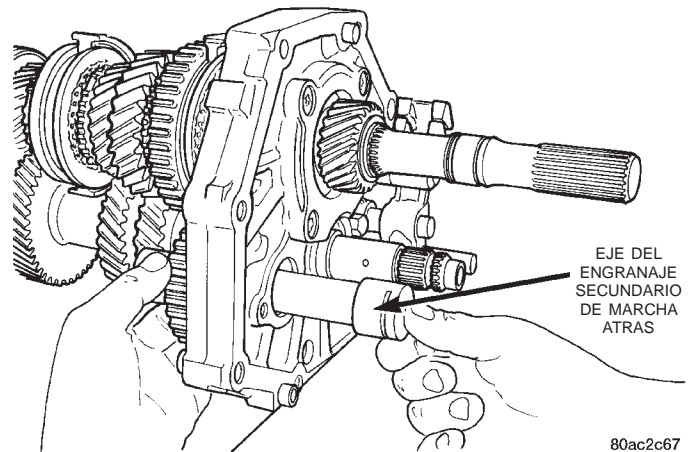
Desmontaje del eje del engranaje secundario de marcha atrás
